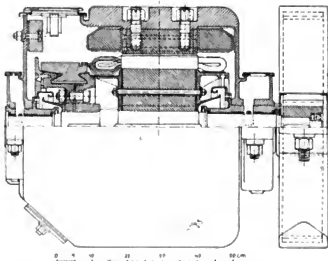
Gleichstrom-Bahnmotor Typ M 13 der Maschinenfabrik Oerlikon.
